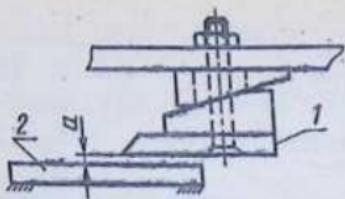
Схема установки зазора между ножом и противорежущей пластиной на косилке измельчитель КИК-1.4:
